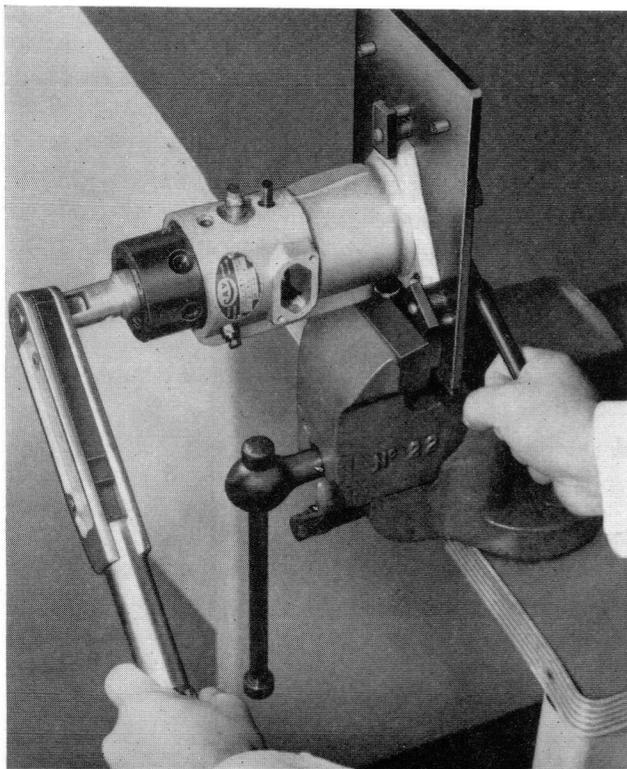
Serrage ou desserrage du rotor de la pompe de transfert
